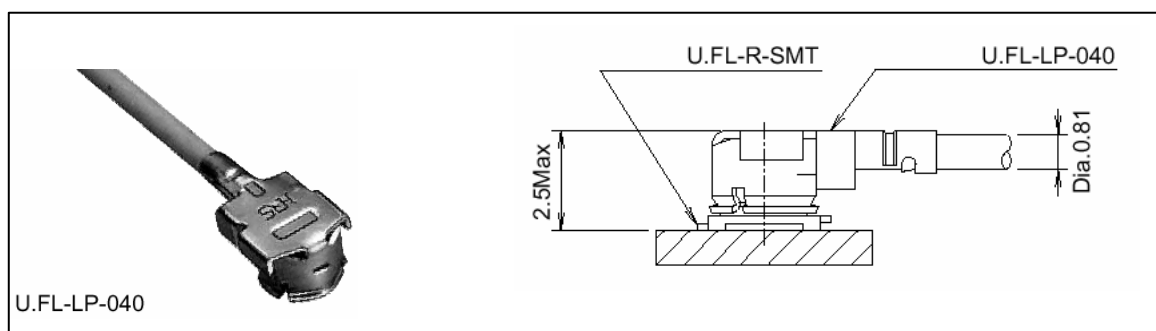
Разъем U.FL-R-SMT с вилкой U.FL-LP-040
